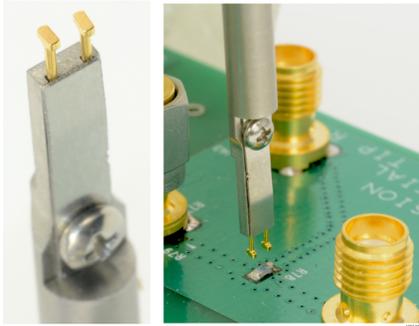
Utilisation de l'outil d'aide à la soudure pour installer les broches carrées sur le circuit imprimé
